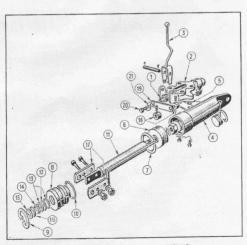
ENSEMBLE VÉRIN - DISTRIBUTEUR - VUE DÉTAILLÉE
